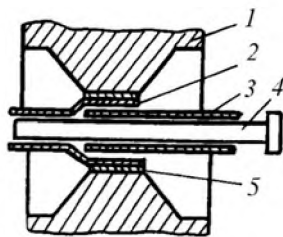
Форма и расположение образцов перед сваркой: 1 – индуктор; 2 – метаемая трубка; 3 – стационарная трубка; 4 – оправка; 5 – изолирующая прокладка
